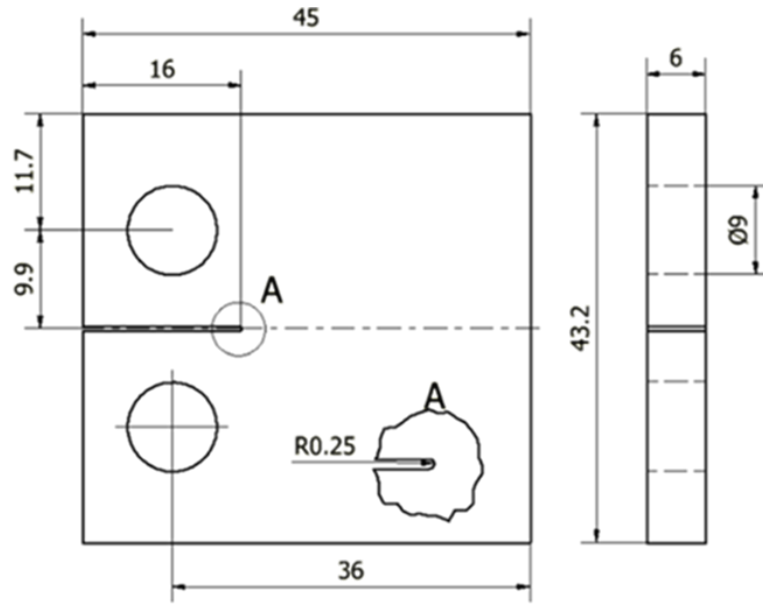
Geometria do provete C(T) (dimensões em mm).
